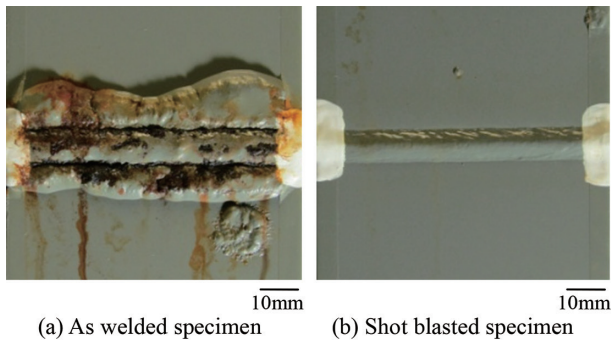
120サイクルのCCT試験後のアーク溶接部外観 (440MPa steel)
